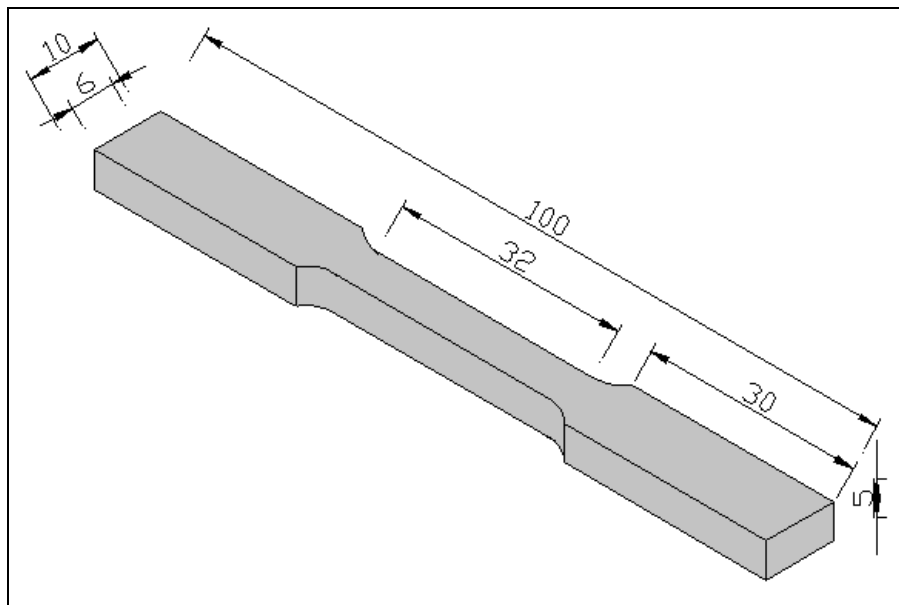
Dimensiones de probeta conforme a norma ASTM [8]
